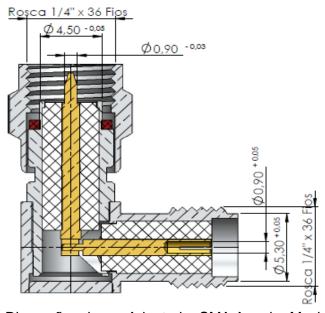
Dimensões de um Adaptador SMA Angular Macho e Fêmea
